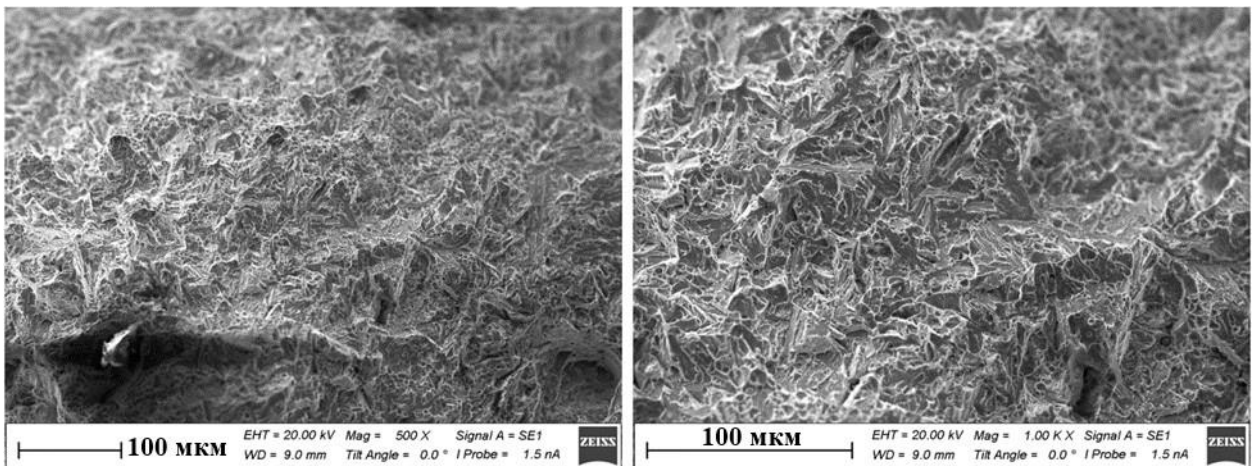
Области квазихрупкого разрушения металла наплавки
